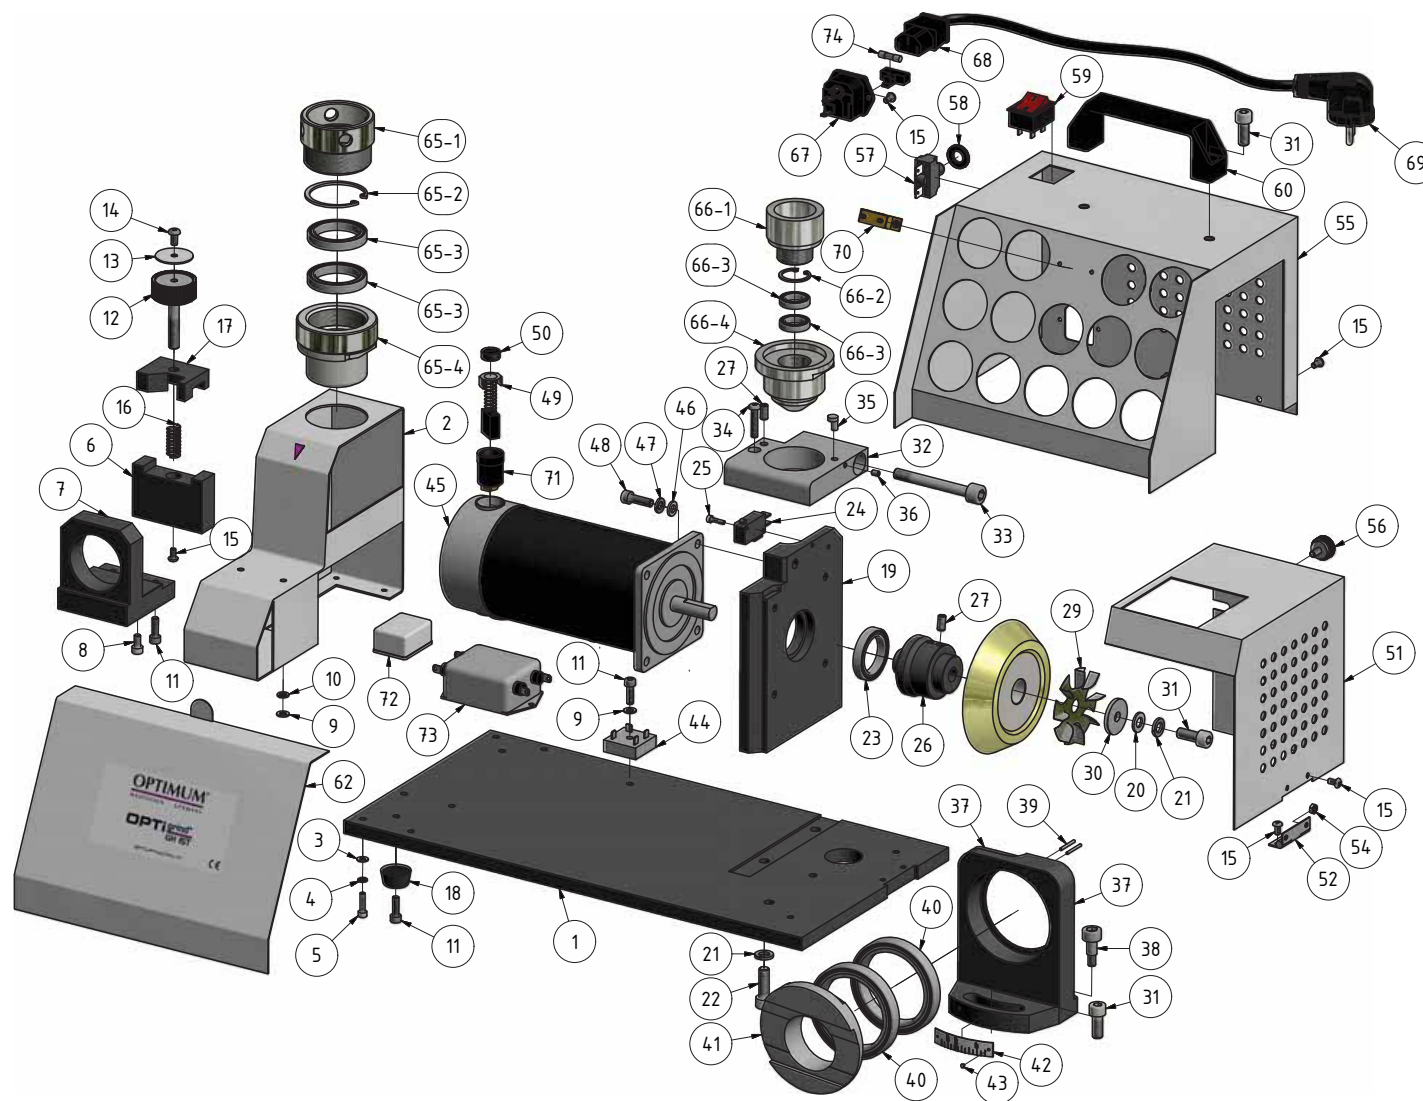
Ersatzteilzeichnung - Drawing spare parts GH15T
